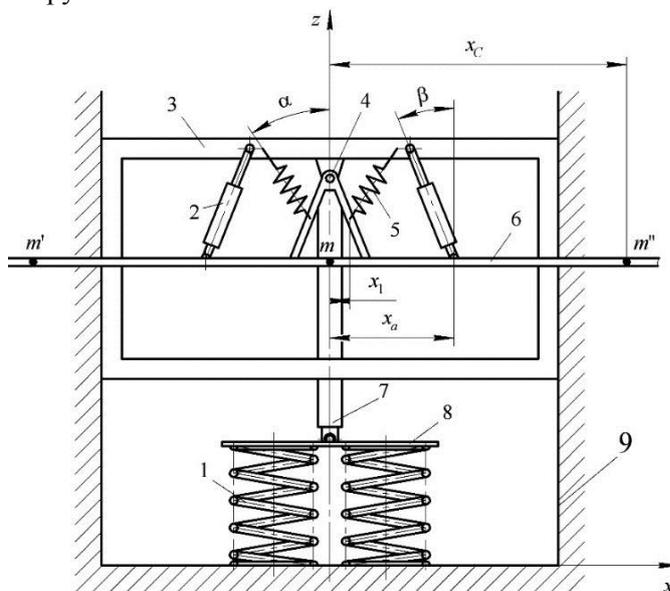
Схема системы стабилизации штанги полевого опрыскивателя
